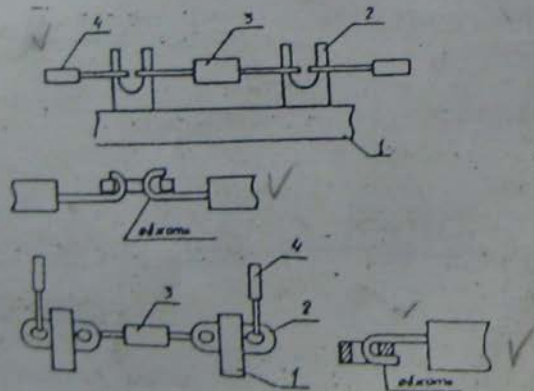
Вариант механического крепления выводов элементов и монтажных проводов на опорных приспособлениях: 1 -монтажная плата; 2 - опорное приспособление; 3 - элемент; 4 - монтажный провод
